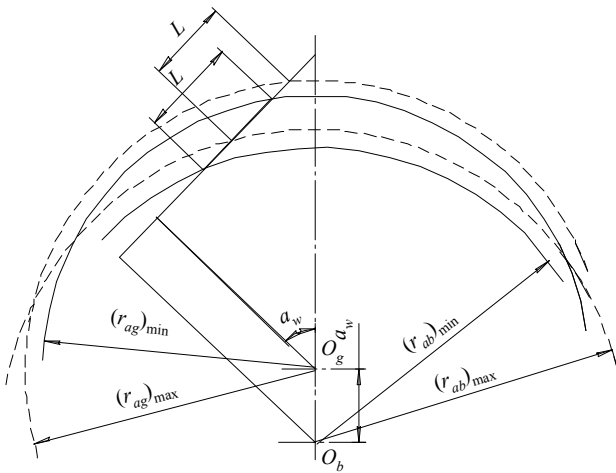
Схема зацепления колес передачи типа К-Н-В
